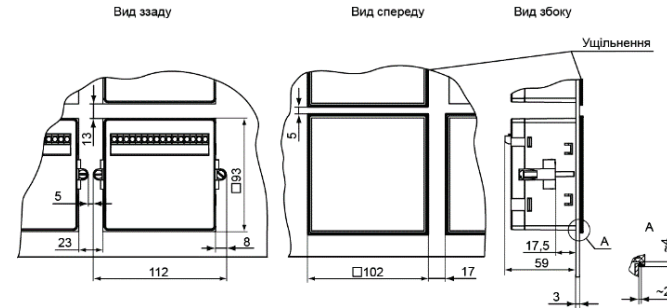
Пристрій у корпусі Щ1, встановлений у щит завтовшки 3 мм
